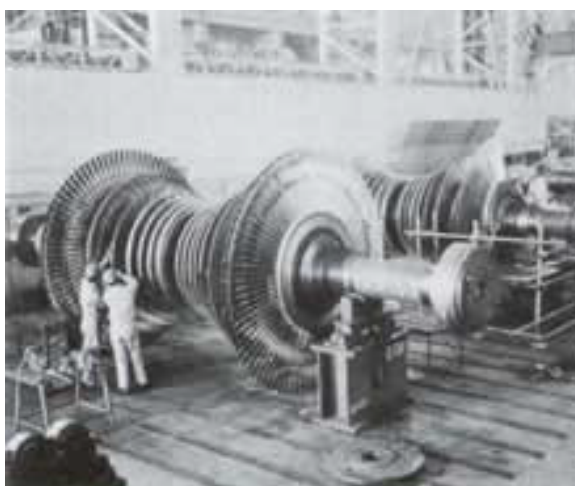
Rotor de unan turbina de vapor de 100 MW [24]
